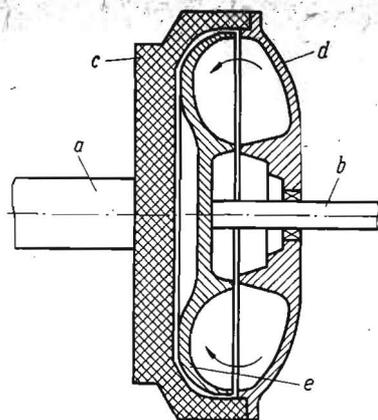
Prinzip der Turbokupplung der VALMET-Waldschlepper; a vom Motor, b zum Getriebe, c Schwungrad des Motors, d Pumpenrad, e Turbinenrad (Weitere Fotos auf der 3. Umschlagseite)
